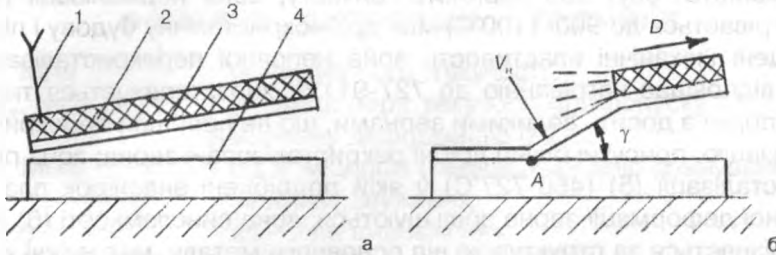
Схема зварювання вибухом: а - вихідне положення, б - процес зварювання
